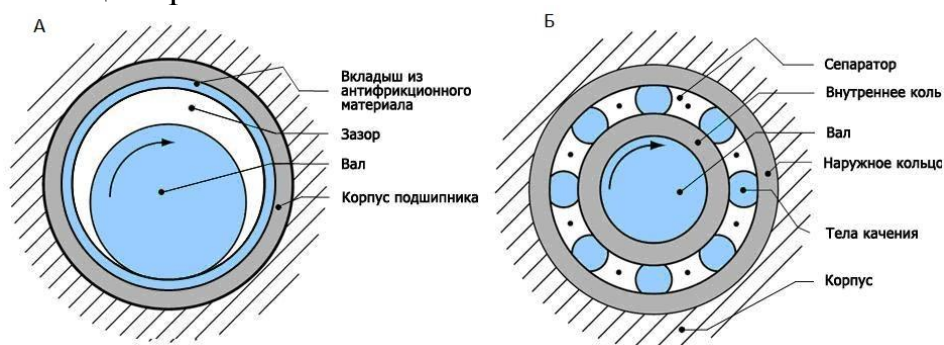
А – подшипник скольжения, Б – подшипник качения
